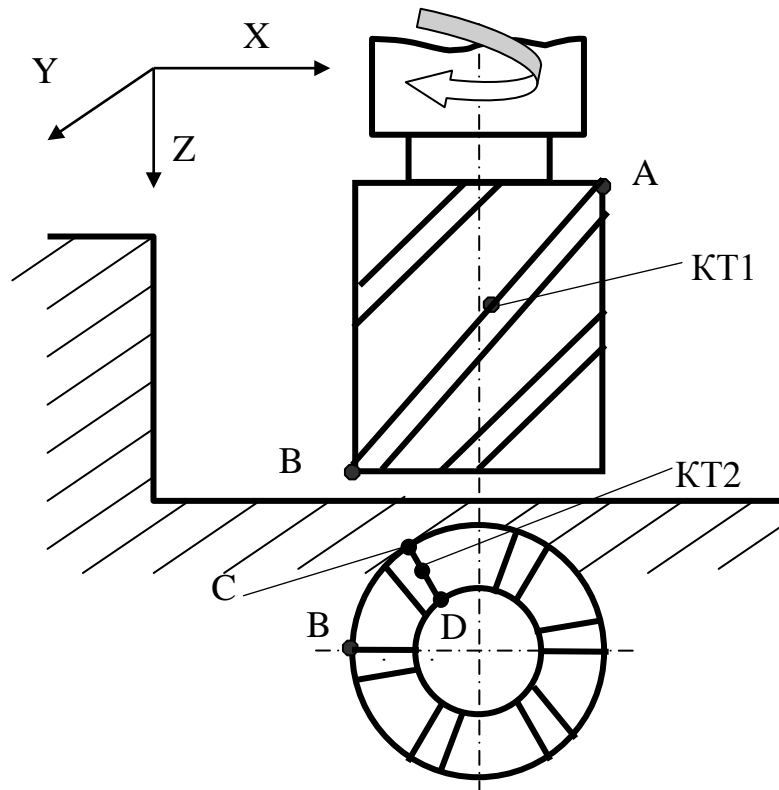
Можливі місця розташування крапки торкання фрези до поверхні обробки
